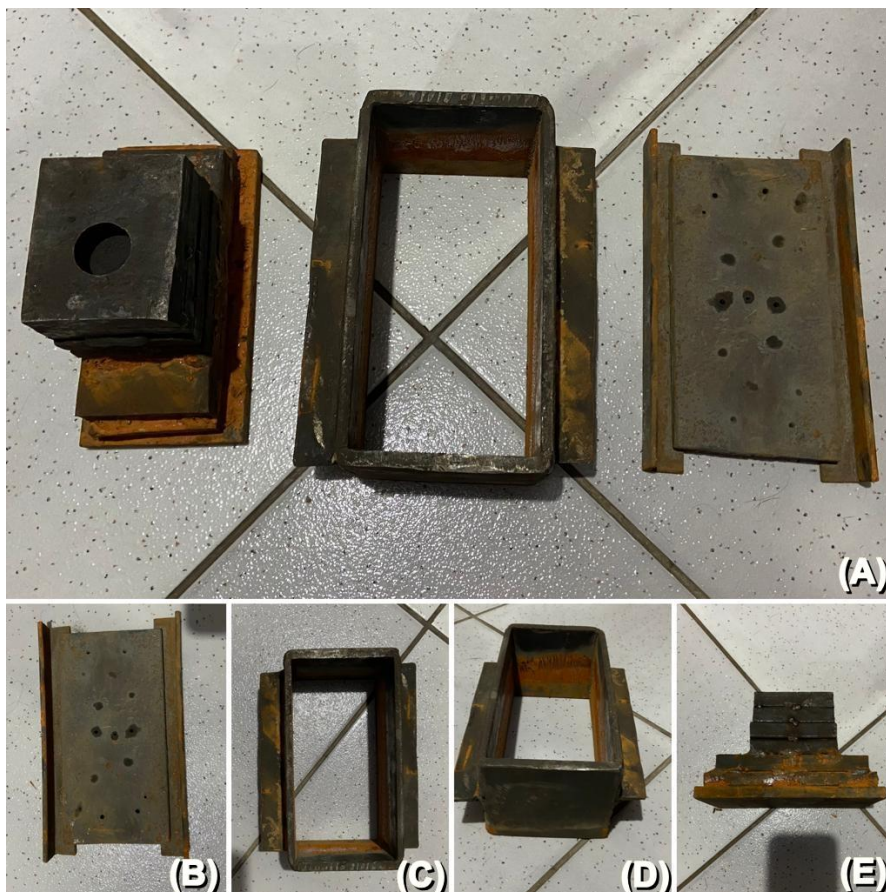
Molde de aço para confecção e moldagem de tijolos maciços. (A): Parte superior, forma e fundo. (B) Fundo falso; (C) e (D) Forma de moldagem com viga I; (E): Cabeçote metálico.
